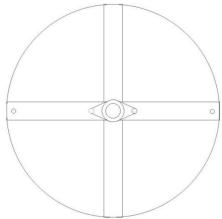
Lubang Besi Plat Tabung Potong 2 buah besi plat dengan panjang 26,5 cm.
